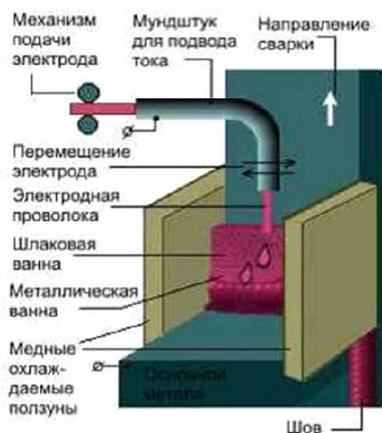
Схема процесса электрошлаковой сварки
